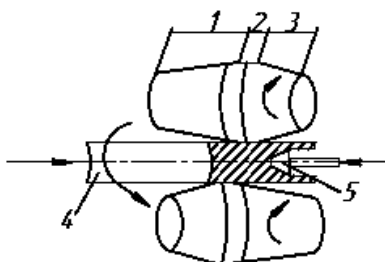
Схема прошивки цилиндрической заготовки: 1 – подготовительный участок; 2 – участок поперечной прокатки; 3 – отделочный участок; 4 – заготовка; 5 – оправка (дорн)
